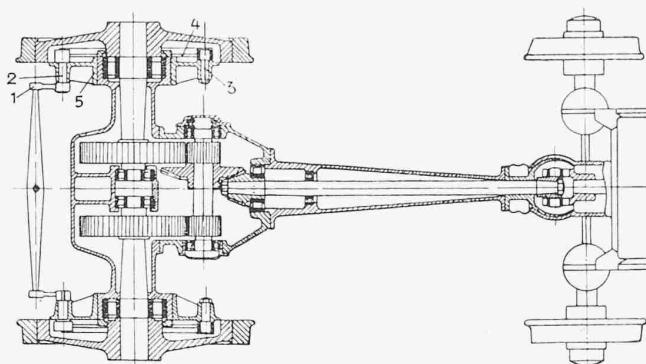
Horizontalschnitt durch Kardan-Antrieb und Bremsvorrichtung.
